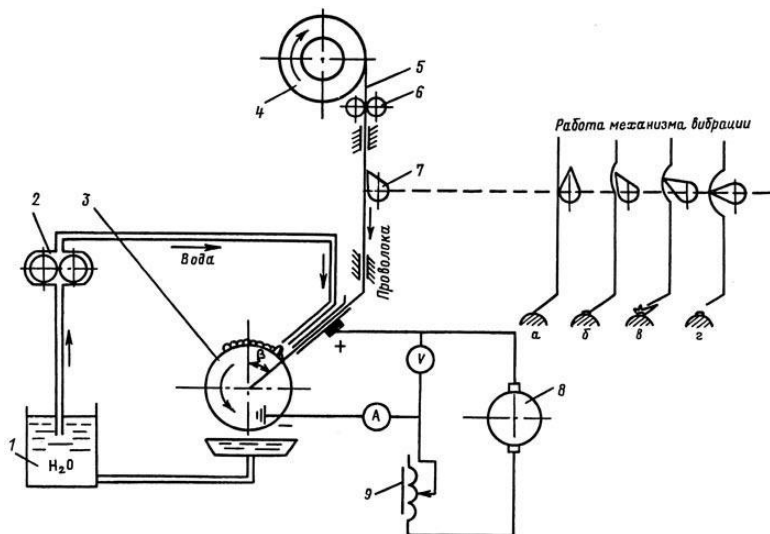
Схема установки для вибродуговой наплавки: 1 - емкость с охлаждающей жидкостью; 2 - водяной насос; 3 - деталь; 4 - кассета с электродной проволокой; 5 - электродная проволока; 6 - ролики подачи проволоки; 7 - механизм вибрации; 8 - источник тока; 9 - регулятор режима наплавки металла; а - контакт электродной проволоки с деталью; б - отрыв электродной проволоки от детали и возникновение дуги; β - процесс наплавки сварочной дугой; z - гашение сварочной дуги
